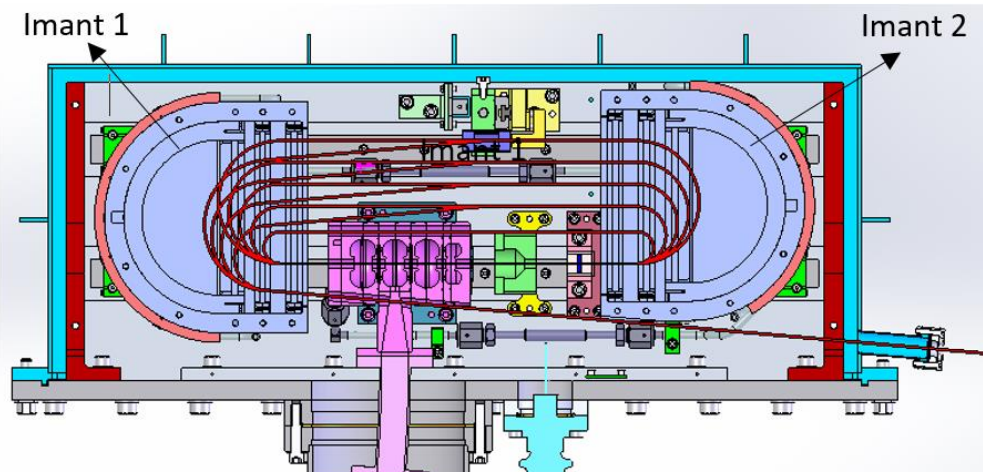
Ubicació dels dos imants en la vista de secció en planta detallada.
